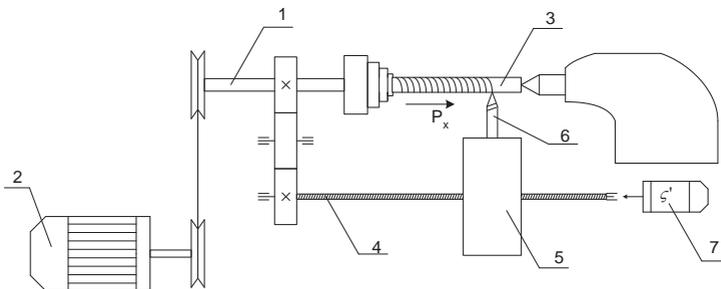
Принципиальная схема встраивания блока коррекции погрешности шага в кинематическую схему станка. 1 - шпиндель станка; 2 - электродвигатель; 3 - заготовка; 4 - ходовой винт станка; 5 - суппорт; 6 - инструмент; 7 - блок коррекции
